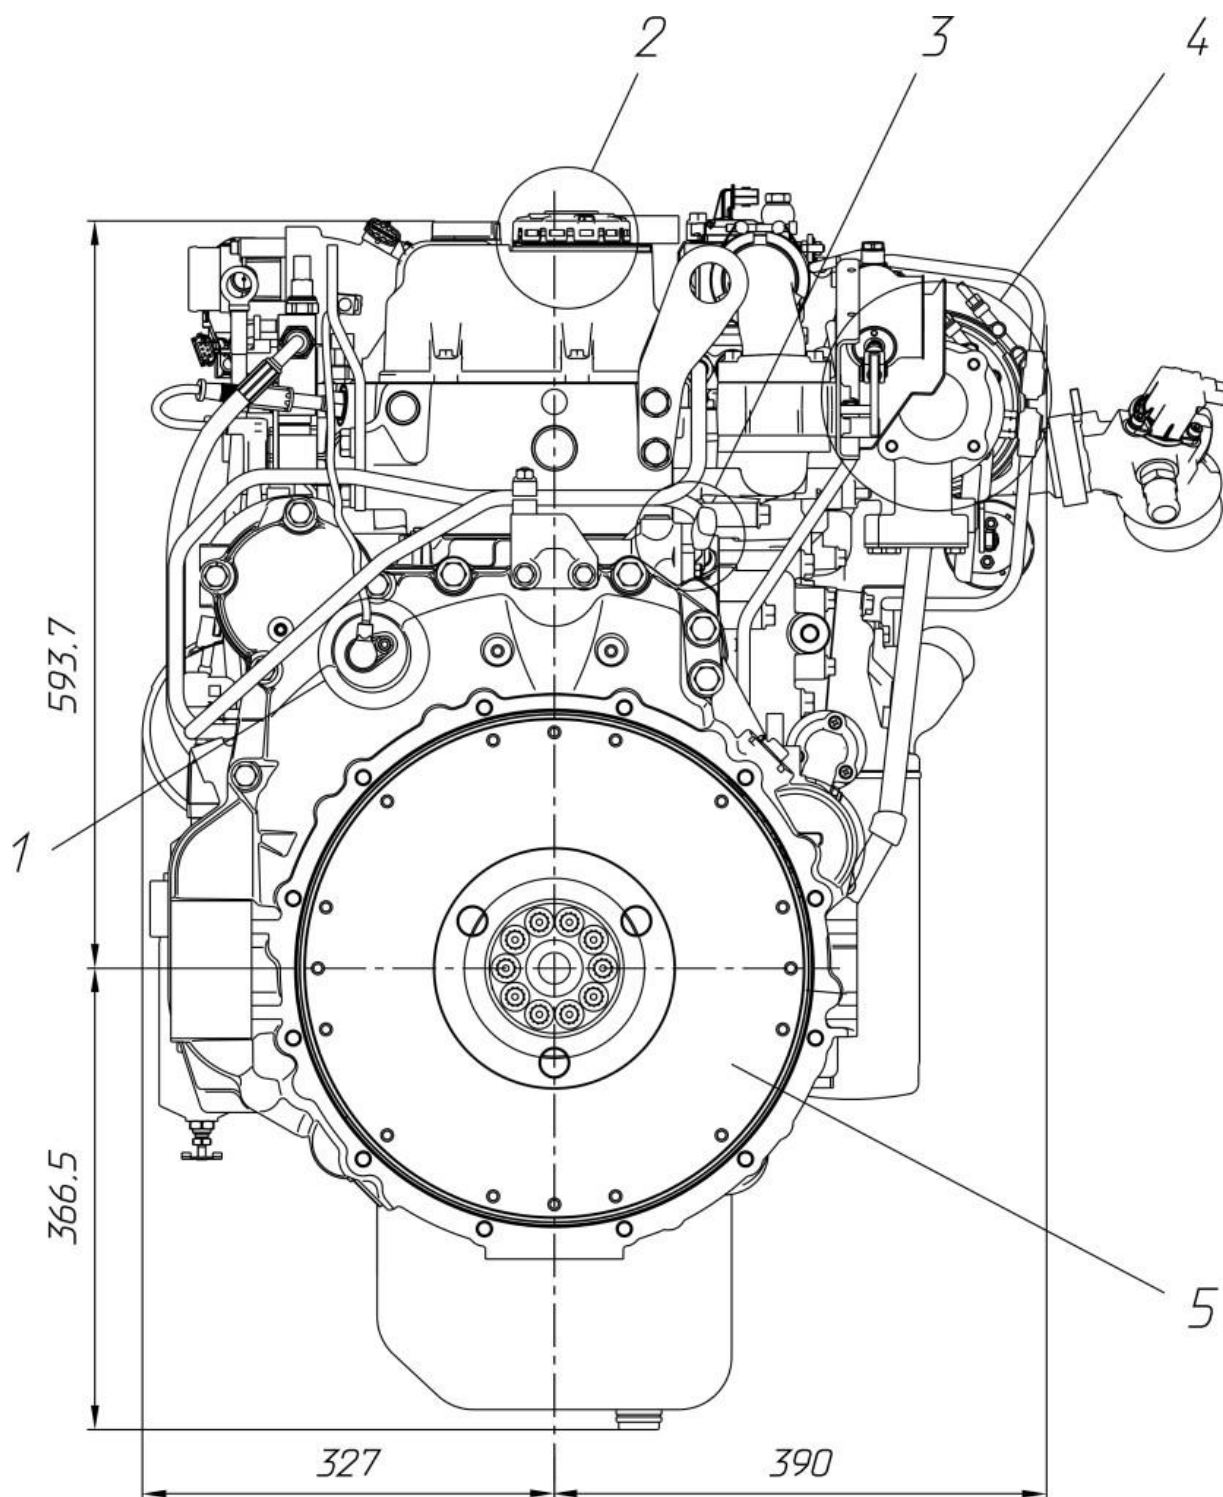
Расположение агрегатов и узлов, габаритные размеры двигателя ЯМЗ-53444-20 (вид сзади):
